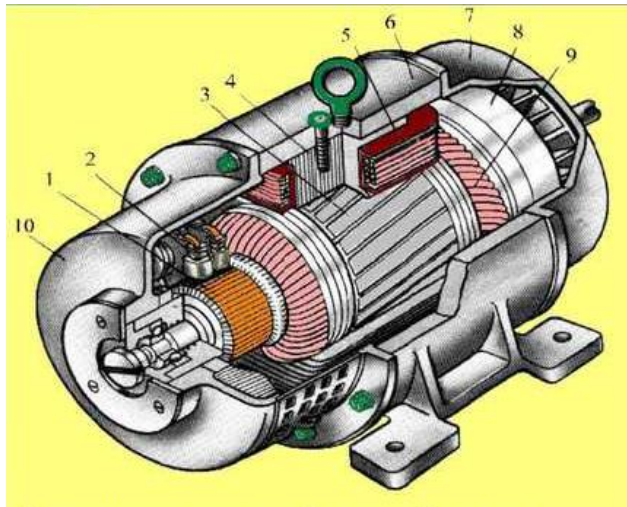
Двигун постійного струму: 1 – колектор; 2 – щітки; 3 – сердечник якоря; 4 – головний полюс; 5 – полюсна котушка обмотки збудження; 6 – станина; 7, 10 – підшипникові щити; 8 – вентилятор; 9 – обмотка якоря
